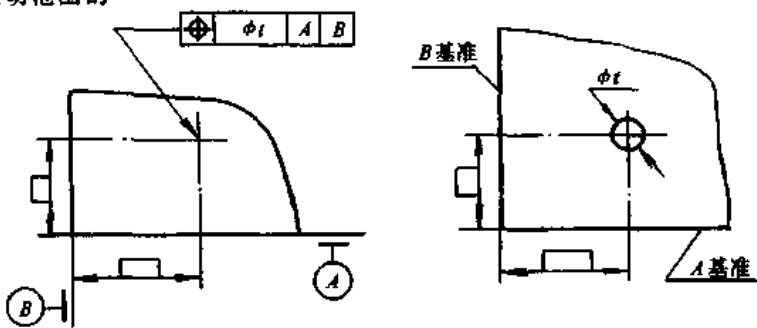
由理论正确尺寸确定公差带位置
